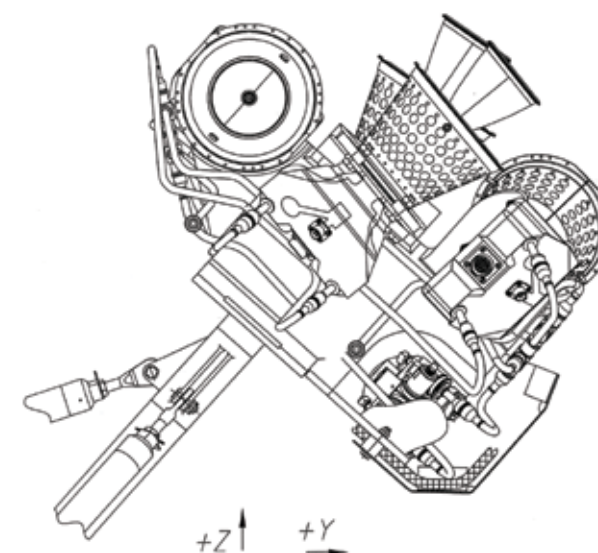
Схема размещения ЖРД на двигательном блоке MBVK82.000.000
